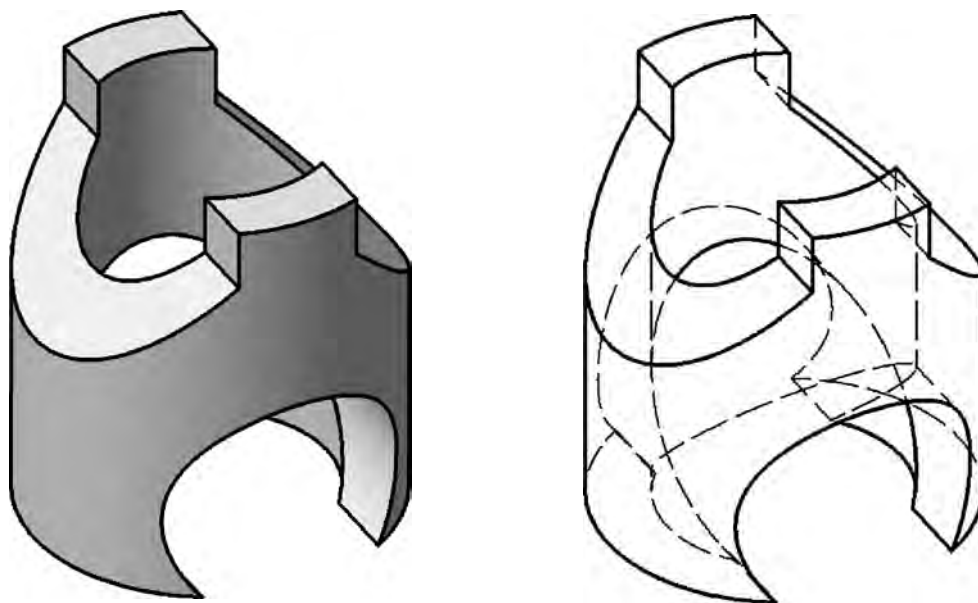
Образец цилиндра (к чертежу на рис. 3.6)
